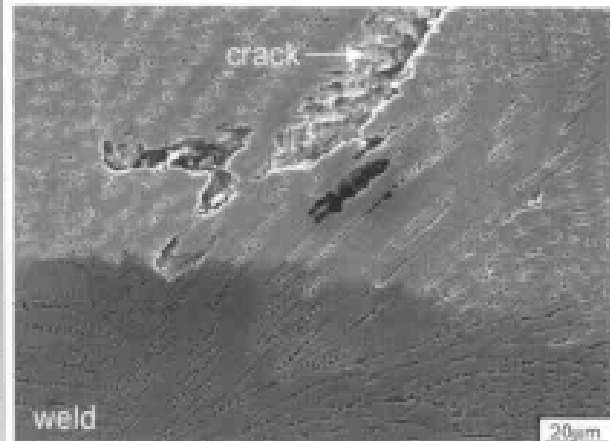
激光焊接, 42CrMo 合金, CO<sub>2</sub> 激光, 功率 2800W, 焊接速度 1.75m/min
